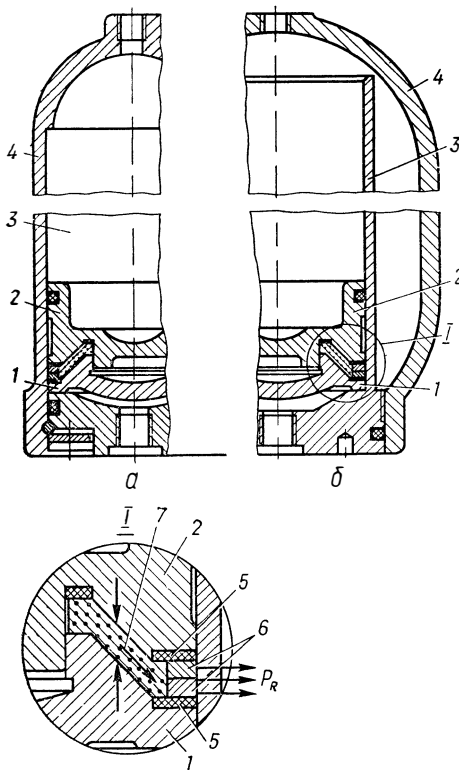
Аккумулятор фирмы «Ате»: *a* — первый вариант конструкции; 1 — нижняя часть поршня; 2 — верхняя часть поршня; 3 — газовая среда; 4 — баллон-цилиндр; *б* — второй вариант конструкции; 1 — нижняя часть поршня; 2 — верхняя часть поршня; 3 — направляющая гильза; 4 — баллон; 5 — упругое кольцо; 6 — уплотнительное кольцо; 7 — уплотнение из эластичной резины
